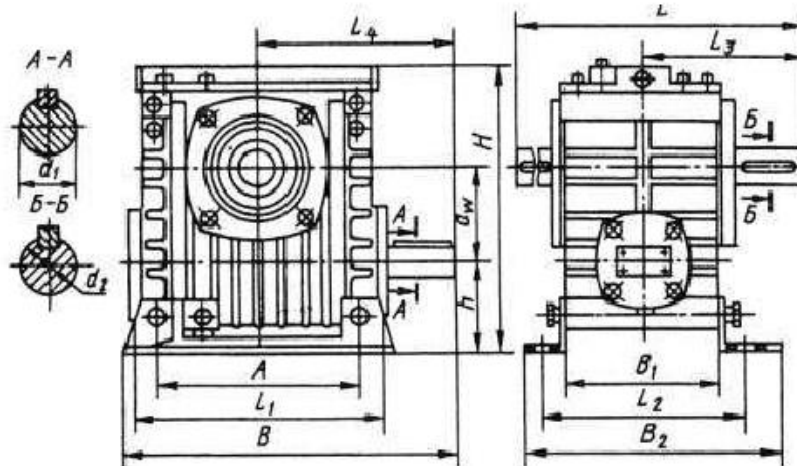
Схема сборки червячного одноступенчатого универсального редуктора (ГОСТ 20373-94)
